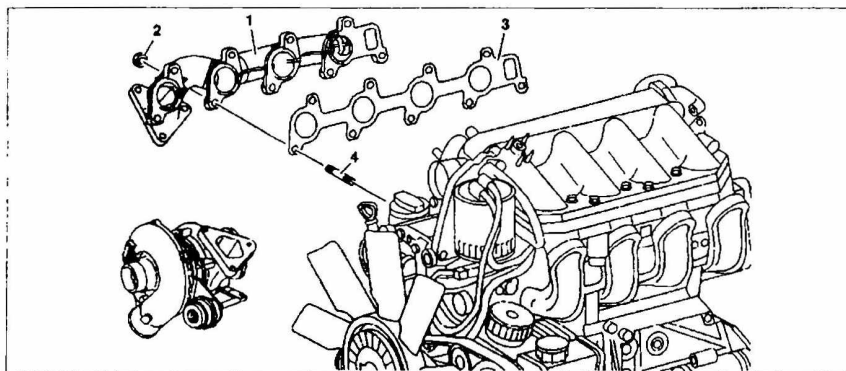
Снятие и установка выпускного коллектора: 1 – Выпускной коллектор; 2 – Гайка; 3 – Прокладка; 4 – Шпилька.
